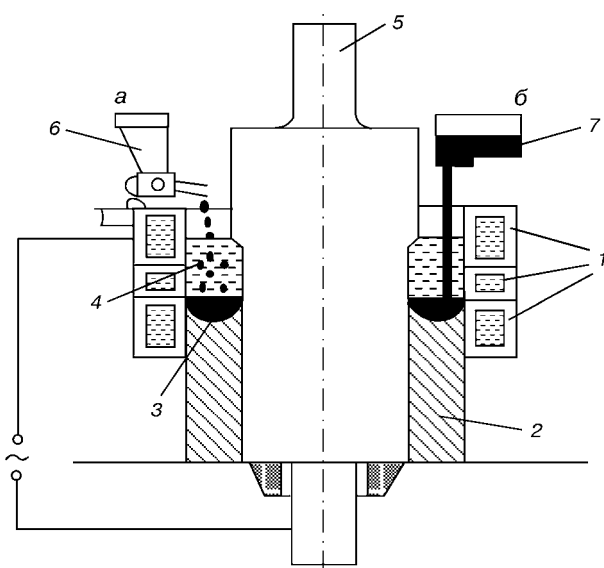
Электрошлаковая наплавка валков в ТПК: *а* — с подачей в шлаковую ванну кускового присадочного материала; *б* — с подачей в шлаковую ванну жидкого металла; обозн. 1–4 см. на рис. 1; 5 — наплавляемая заготовка; 6 — дозатор подачи кускового материала; 7 — емкость для подачи жидкого металла
